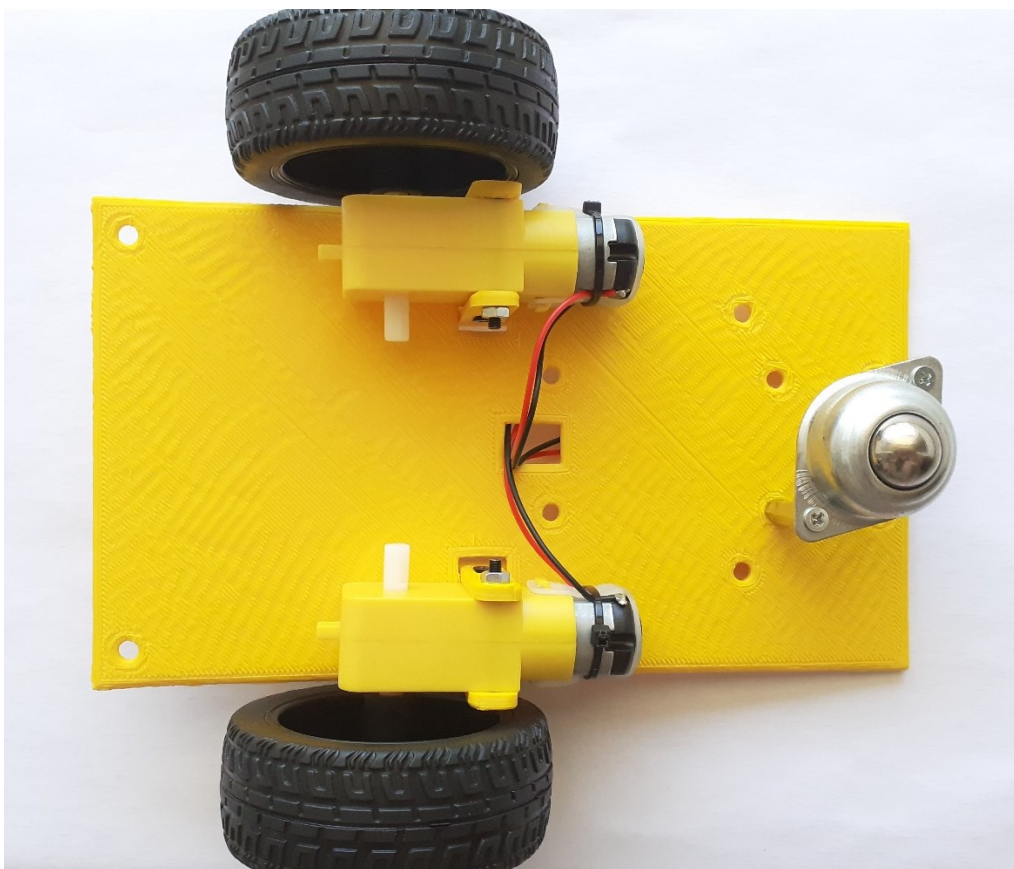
La voiture robotique DIY après avoir placé la dernière pièce sur le dessous du châssis
